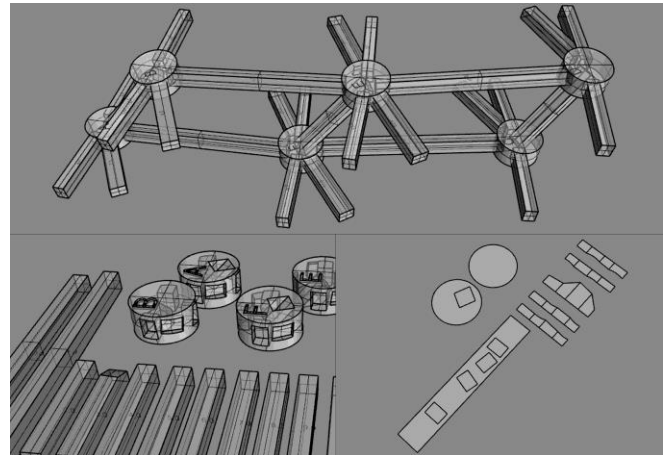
Identificação e planificação automatizada das geometrias de peças a serem calandradas e dobradas
